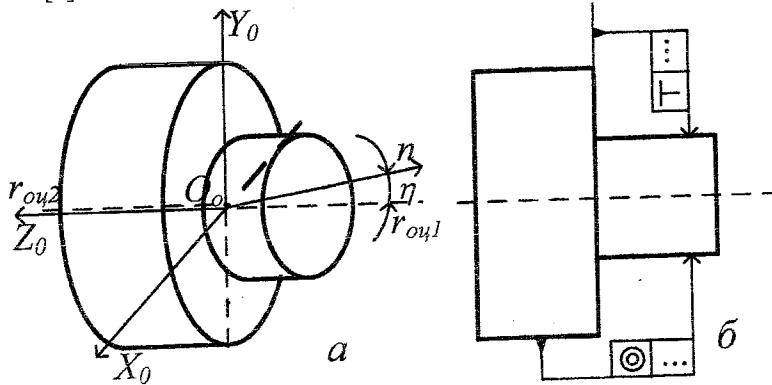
Обрабатываемая на токарном станке деталь
